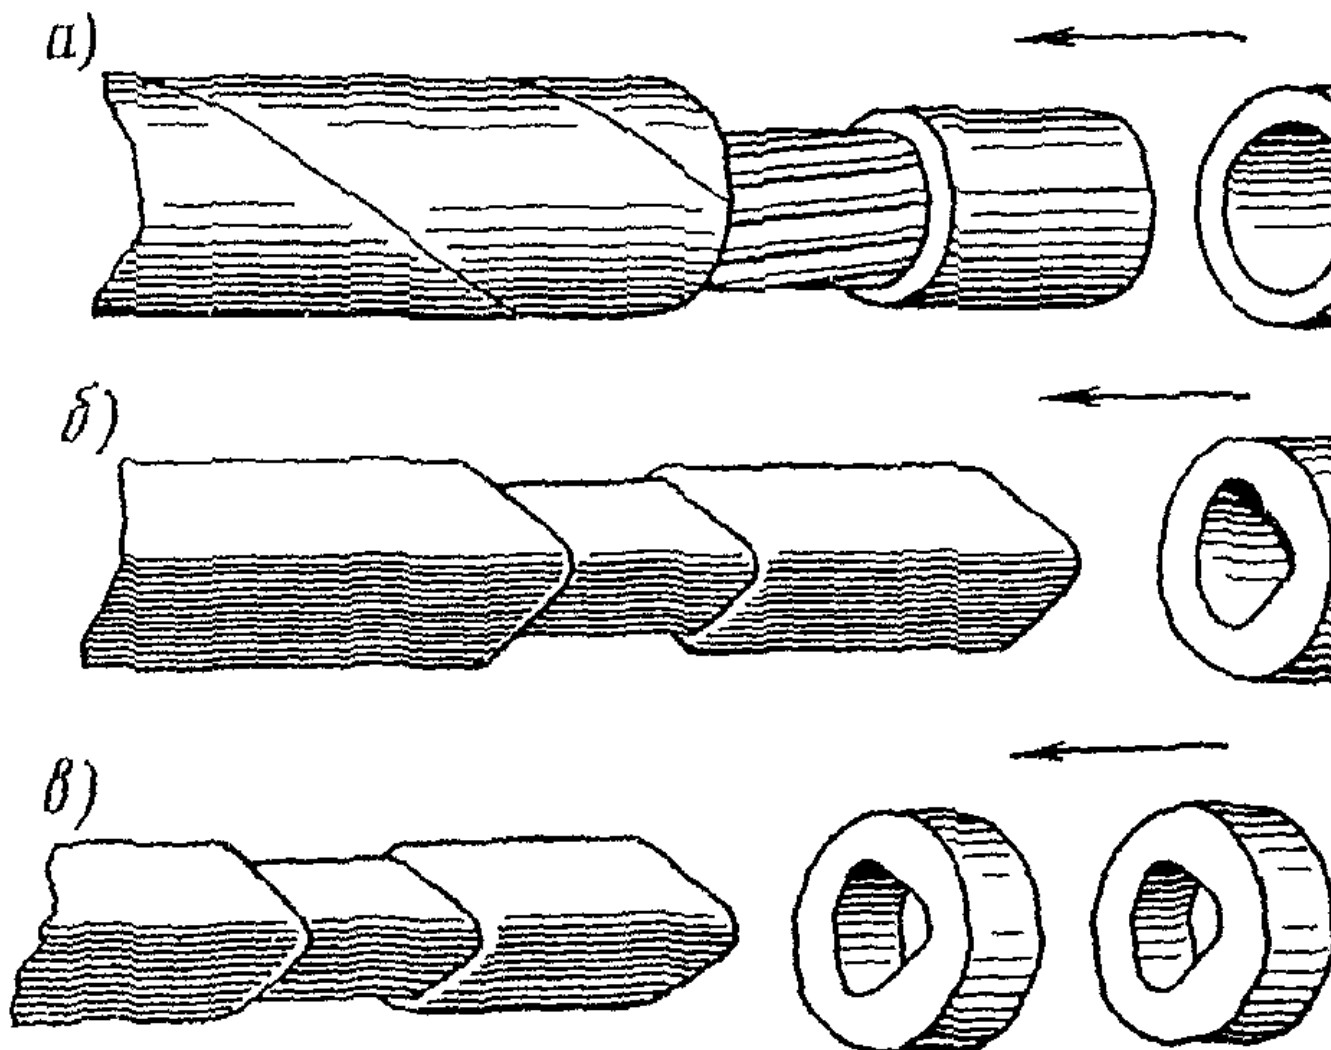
Колпачки, втулки и шайбы для защиты поверхностей жил от обгорания при сварке: а - колпачок для многопроволочной жилы; б - втулка для секторной однопроволочной жилы; в - шайба для секторной однопроволочной жилы
